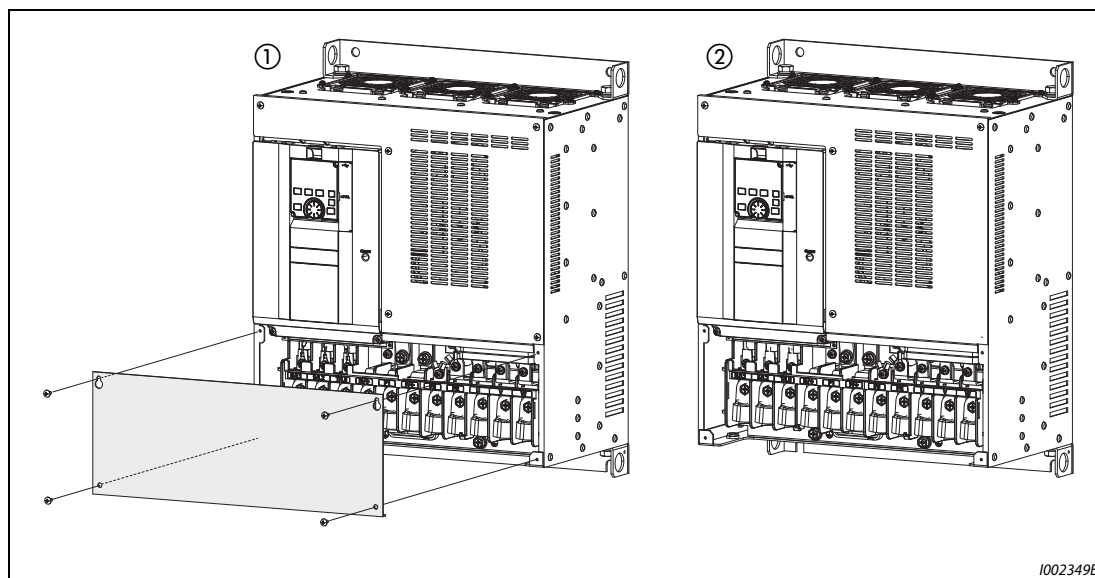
Установка передней панели и крышки клеммного блока
